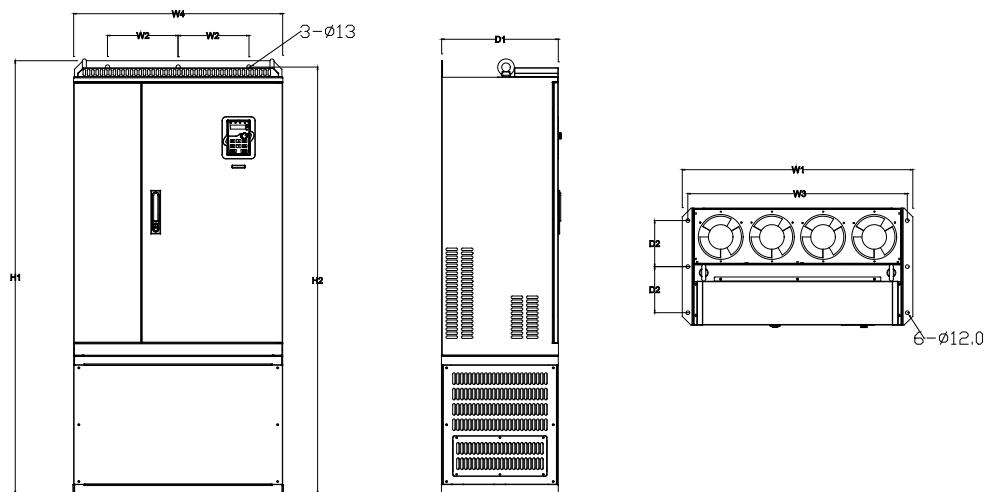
Напольный монтаж 220 – 315 кВт
